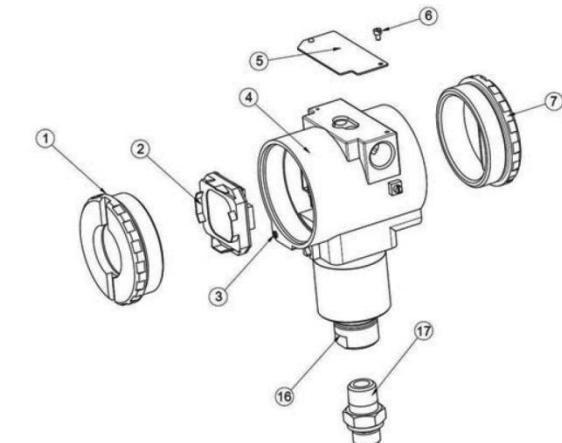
Основные элементы конструкции датчика HMP 331D.
